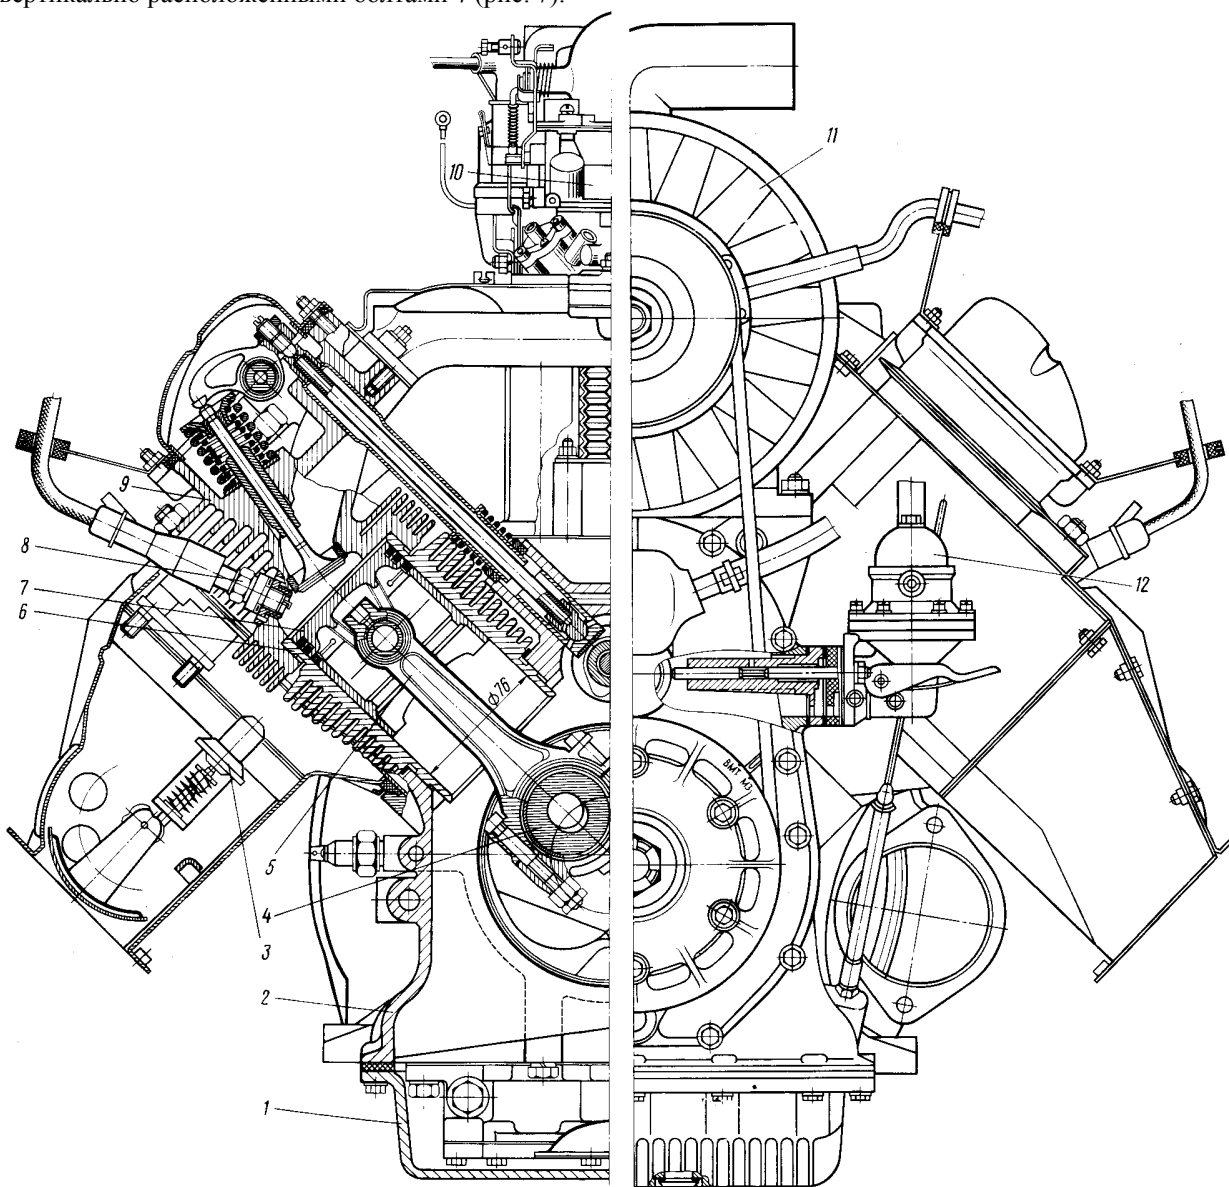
Поперечный разрез двигателя: 1 — масляный поддон; 2 — картер коленчатого вала; 3 — термостат; 4 — коленчатый вал; 5 — шатун; 6 — цилиндр; 7 — поршень; 8 — свеча; 9 — головка цилиндров; 10 — карбюратор; 11 — направляющий аппарат вентилятора с рабочим колесом и генератором в сборе; 12 — топливный насос.
